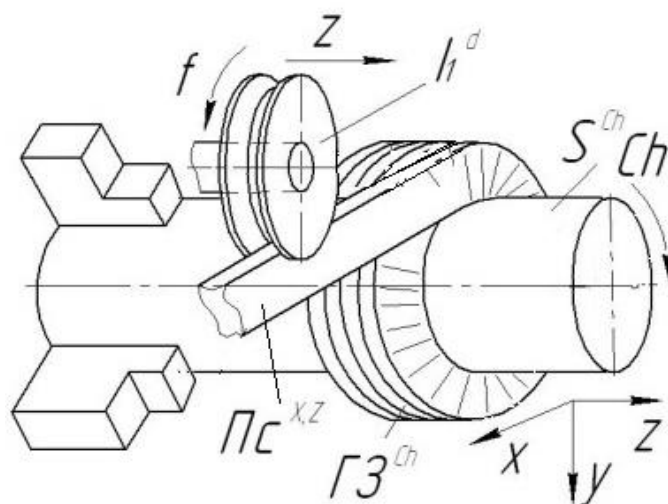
Виготовлення гвинтової заготовки способом навивання смугової заготовки ребром на оправу: ГЗ – гвинтова заготовка, Пс – смугова заготовка, I_1 – згинний ролик.
